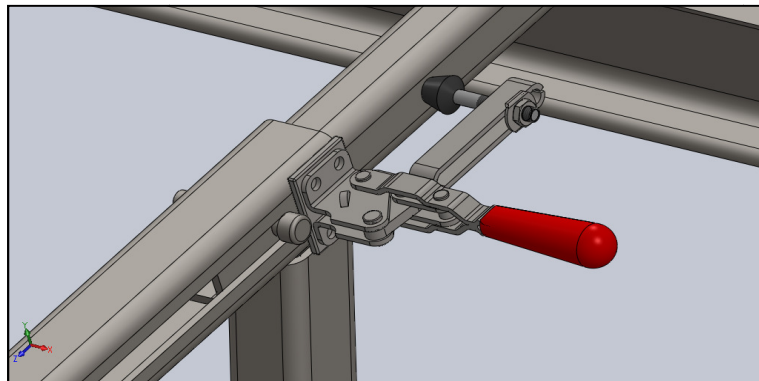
Dispositivo de fixação da estrutura telescópica modelado no Solidworks®.
